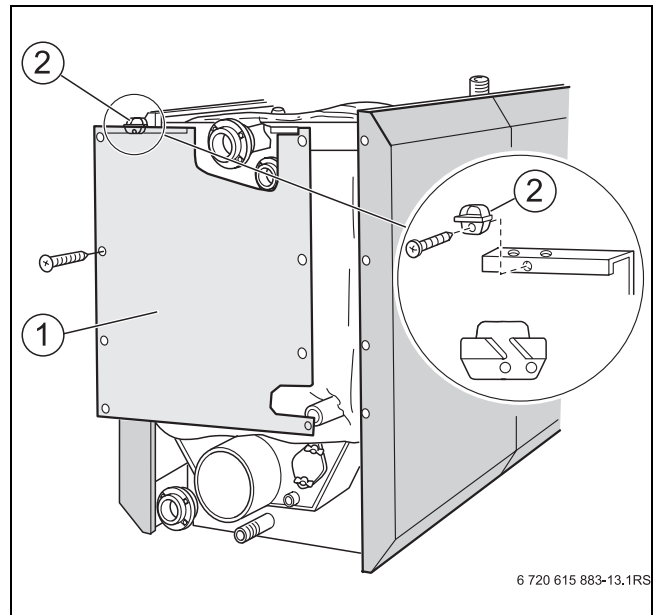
Крепление задней стенки (котлы от 400 до 640 кВт)
